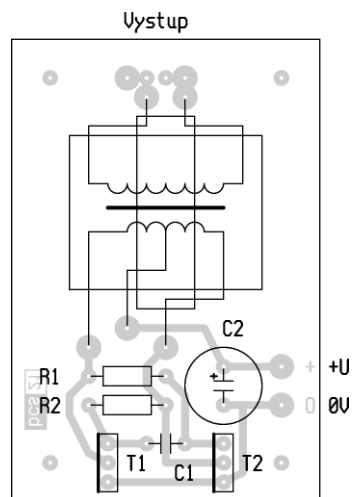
Deska s plošnými spoji pro měnič z obr. 1 v měřítku 1:1 a rozmístění součástek na desce
